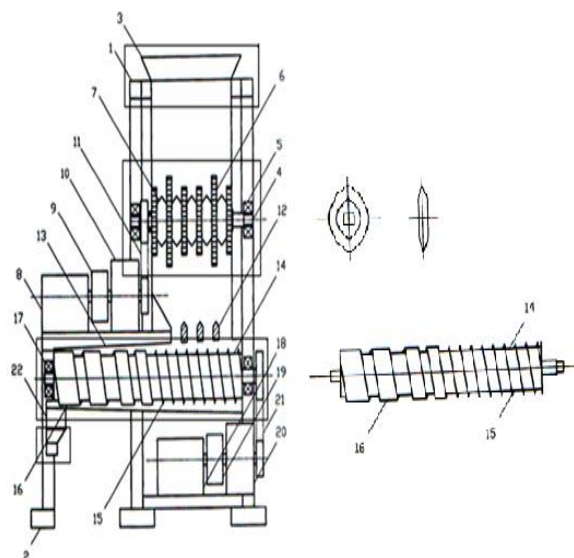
Машина для резки и измельчения рогов домашнего северного оленя Эвенкийской породы
